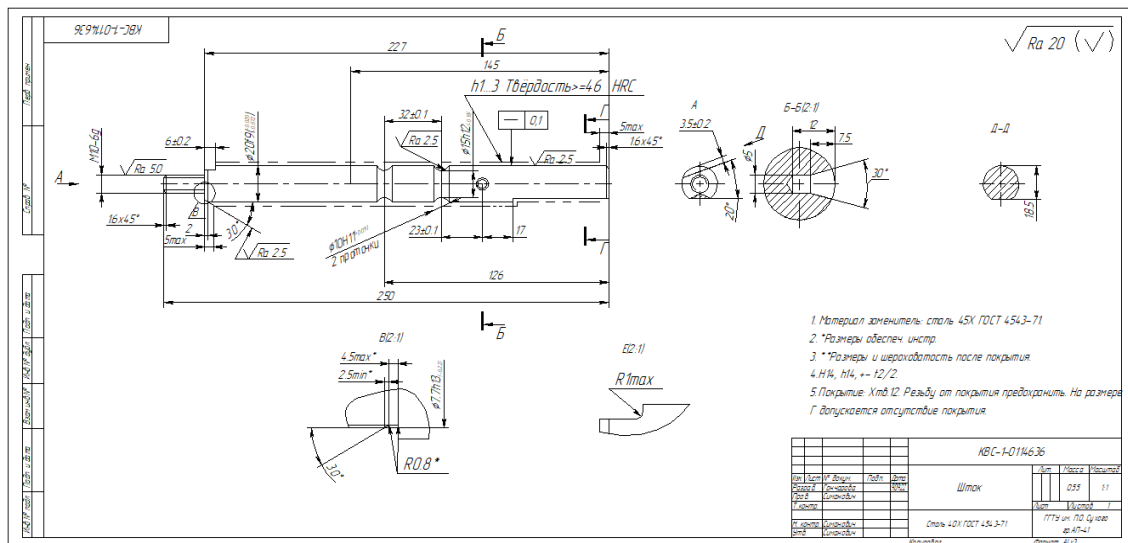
2D-чертеж детали шток KBC-1-0114636 с ассоциативной связью с 3D-моделью
